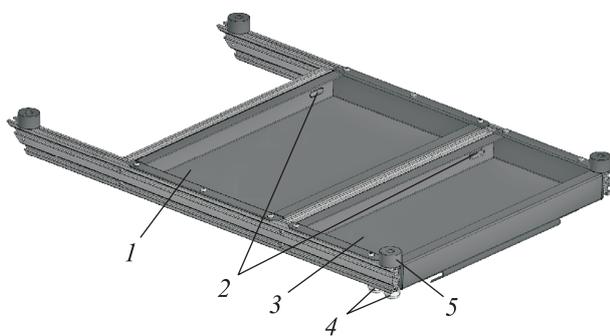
Цифровой двойник несущей рамы принтера: 1 и 3 — центральный и передний ящики для электроники; 2 — кожухи пазов; 4 — сальники PG9; 5 — прорезиненные подставки
